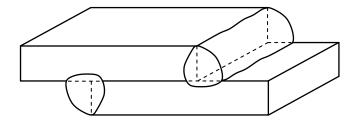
Junta de solape con doble soldadura de filete
